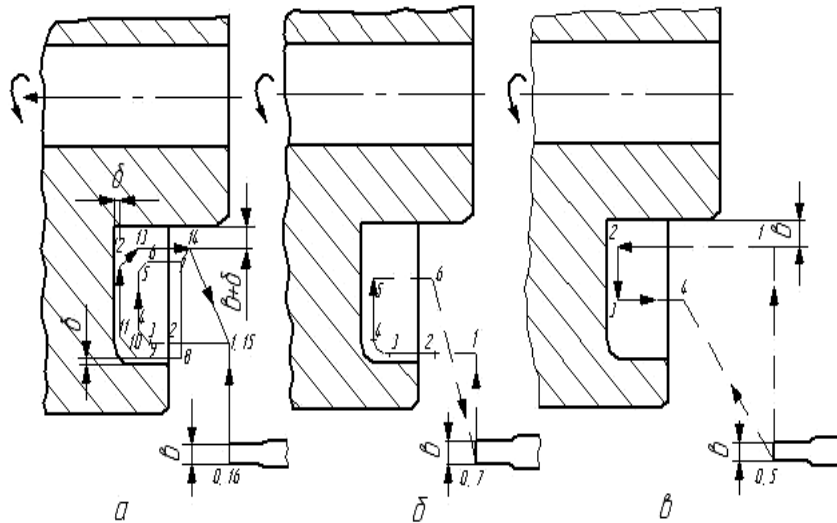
Схема обробки торцевої канавки: а - чорновий; б, в - чистові робочі ходи (в - ширина ріжучої кромки; δ - припуск на чистову обробку)
